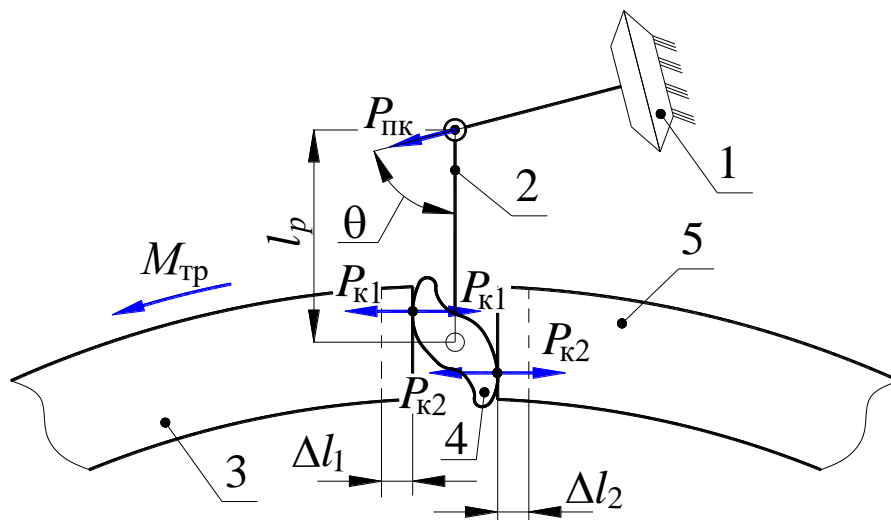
Розрахункова схема кулачкового механізму розтиску:
